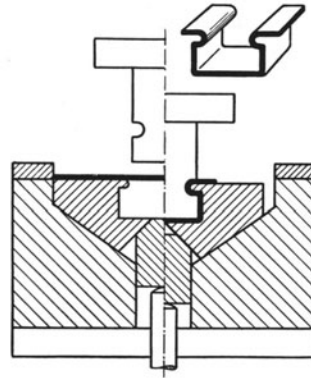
Werkzeug mit schräg geführten Biegestempeln
